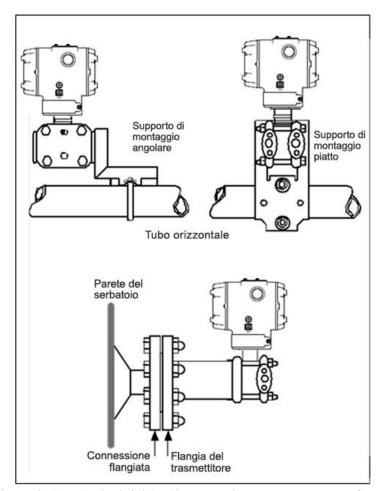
Installazioni tipiche di montaggio con supporto e con flangia
